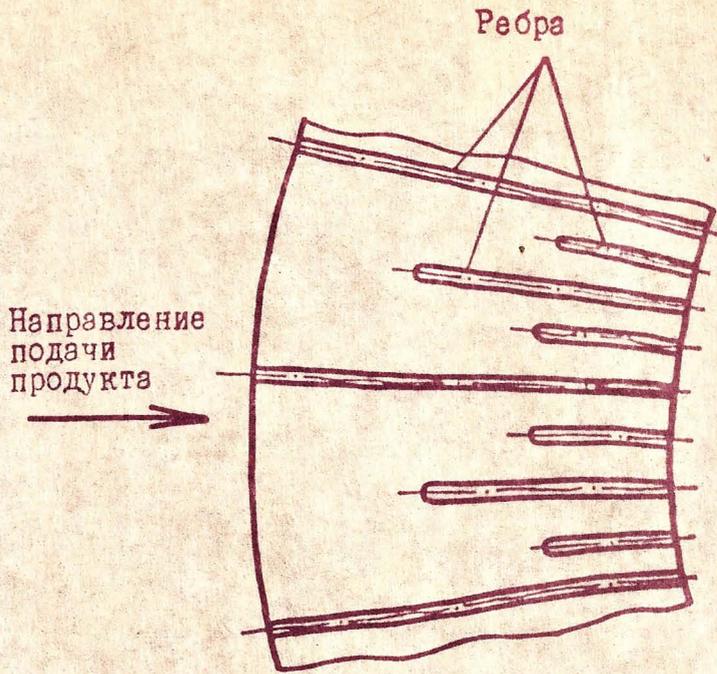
Развертка рабочей части корпуса с переменным числом ребер (ребрами разной длины)
